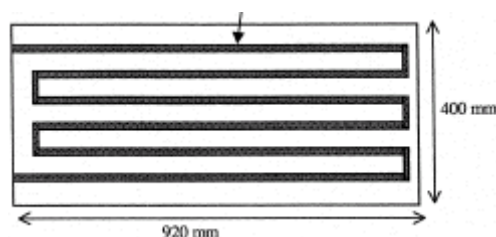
Sistema de aquecimento posicionado em uma das placas do molde.
